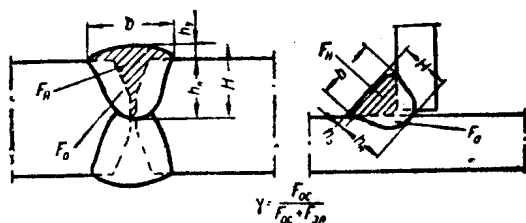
熔剂下焊接时焊缝的主要尺寸
